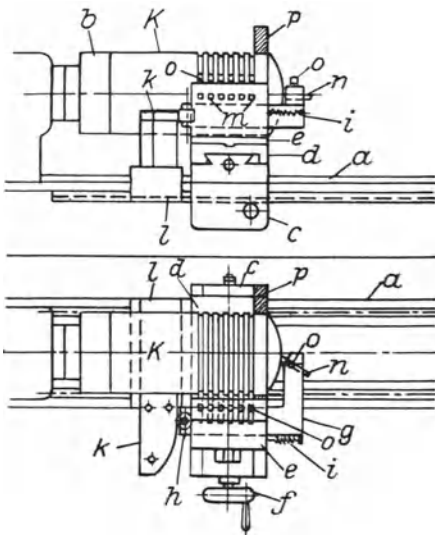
Bearbeitung eines Motorkolbens durch kombinierte Stahlhalter.
